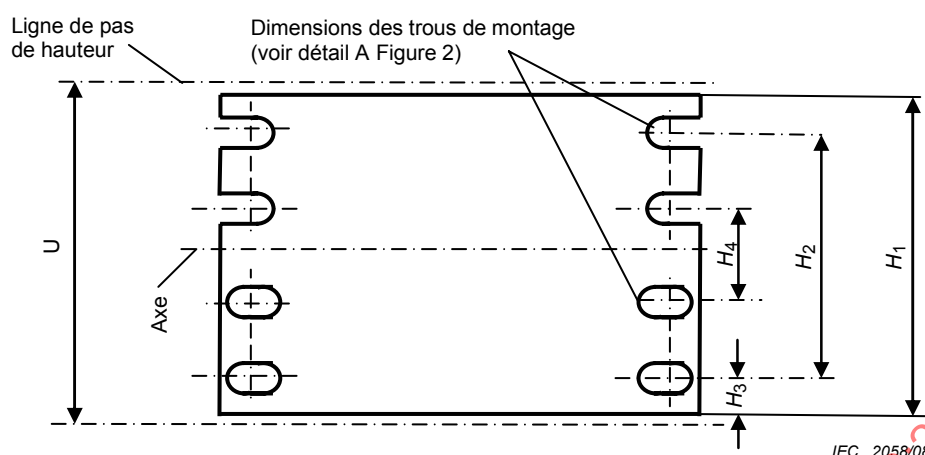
Dimensions des panneaux avant de 6U à 12U
